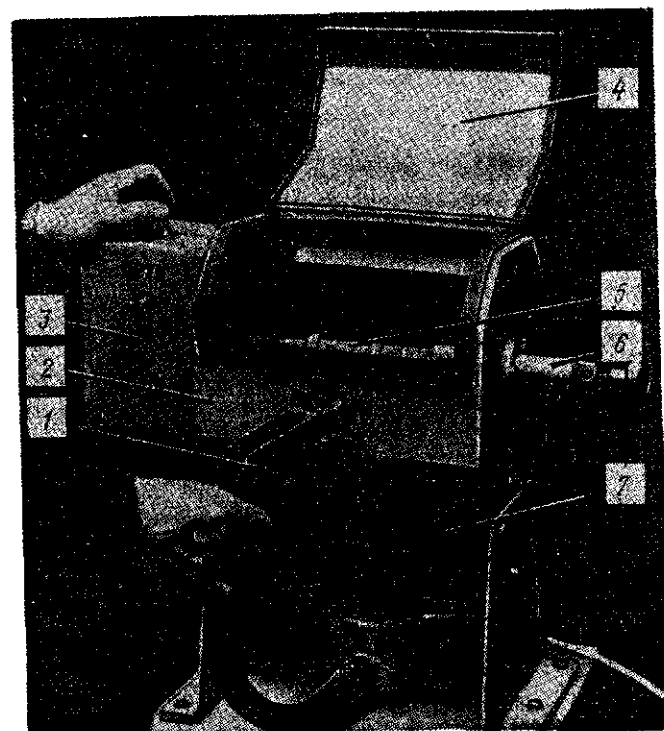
Аппарат для дробеструйной обработки круглых деталей перед нанесением газотермических покрытий:
